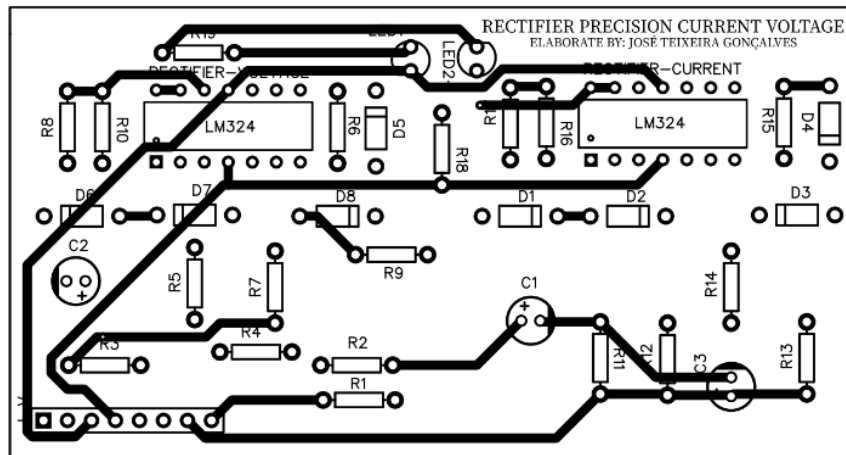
Placa PCB da camada superior do retificador de precisão.
